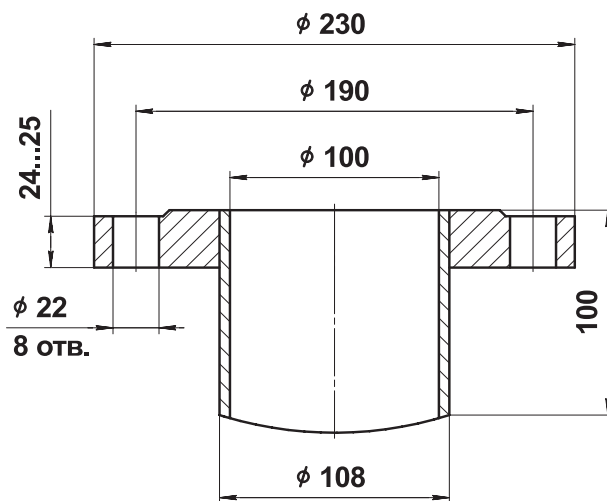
Размеры приварного патрубка на давление 2,5 МПа
